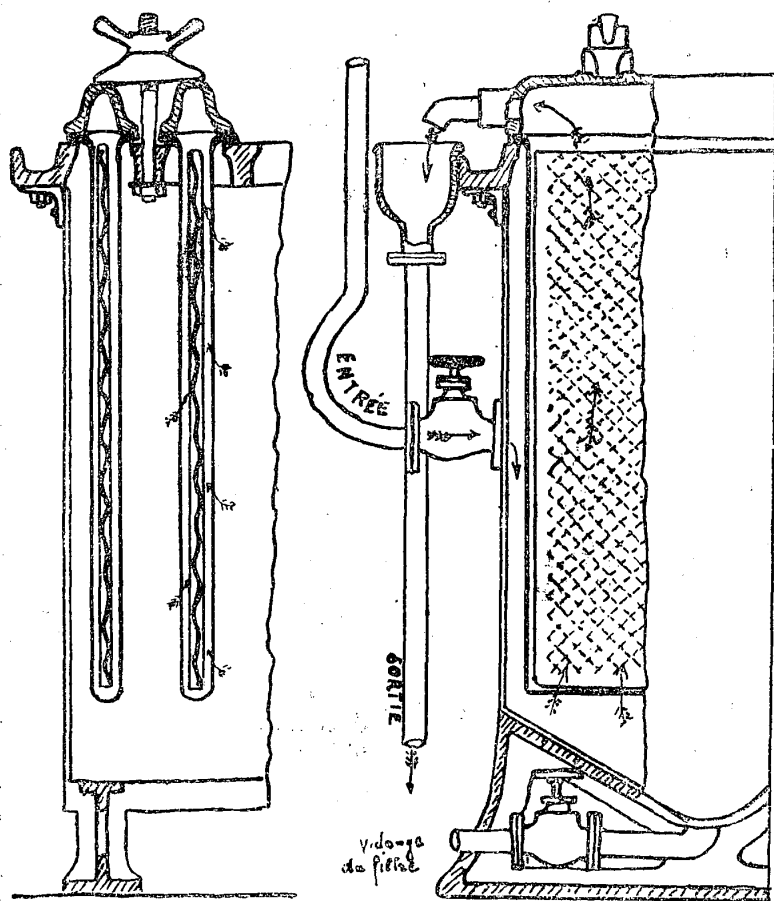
VUE EN COUPE D'UN FILTRE MÉCANIQUE
